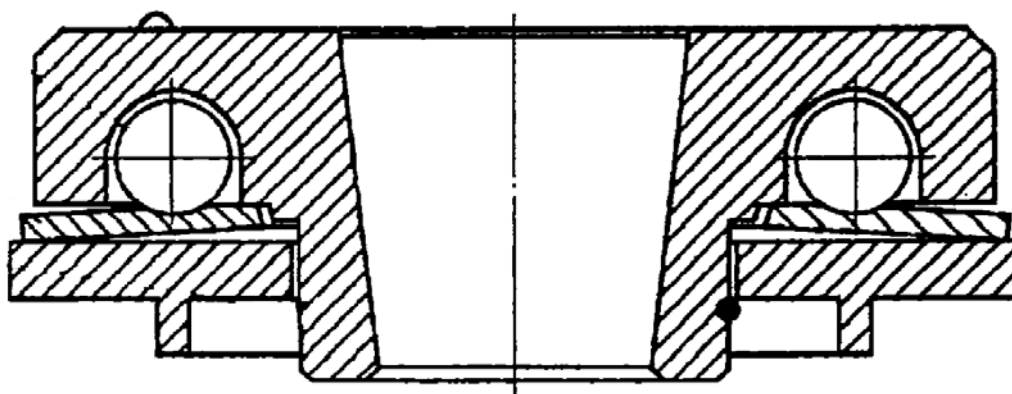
Механізм повертання клапанів типу «ротокап»
